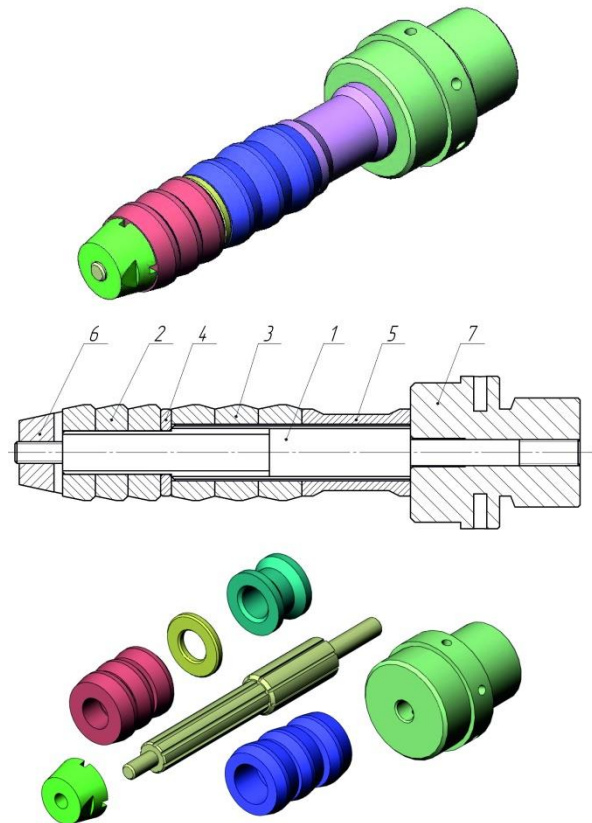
Схема деформуючої протяжки для обробки круглих отворів: 1 - оправка; 2 - перший блок деформуючих елементів; 3 - другий блок деформуючих елементів; 4 та 5 - дистанційні втулки 6 - конусна гайка; 7 - хвостовик
